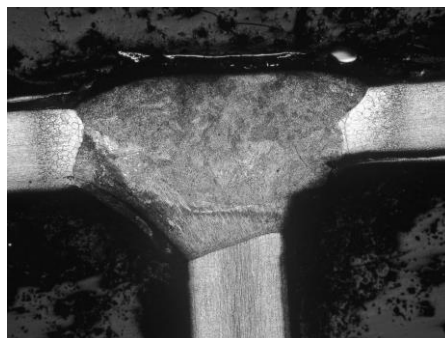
Общий вид сварного соединения после ремонтной сварки
